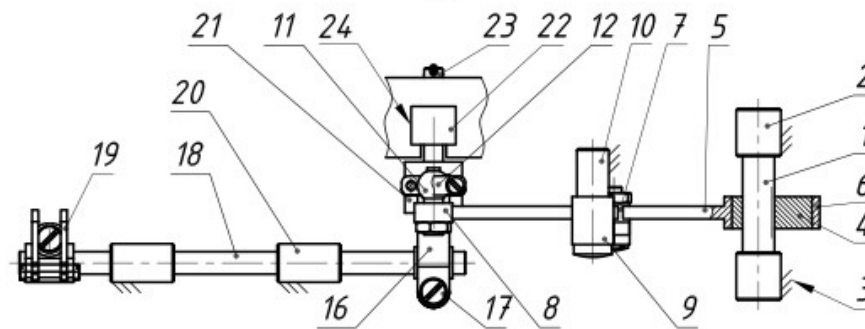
Механізм петельника швейної машини з П-подібною платформою (вид зверху)
